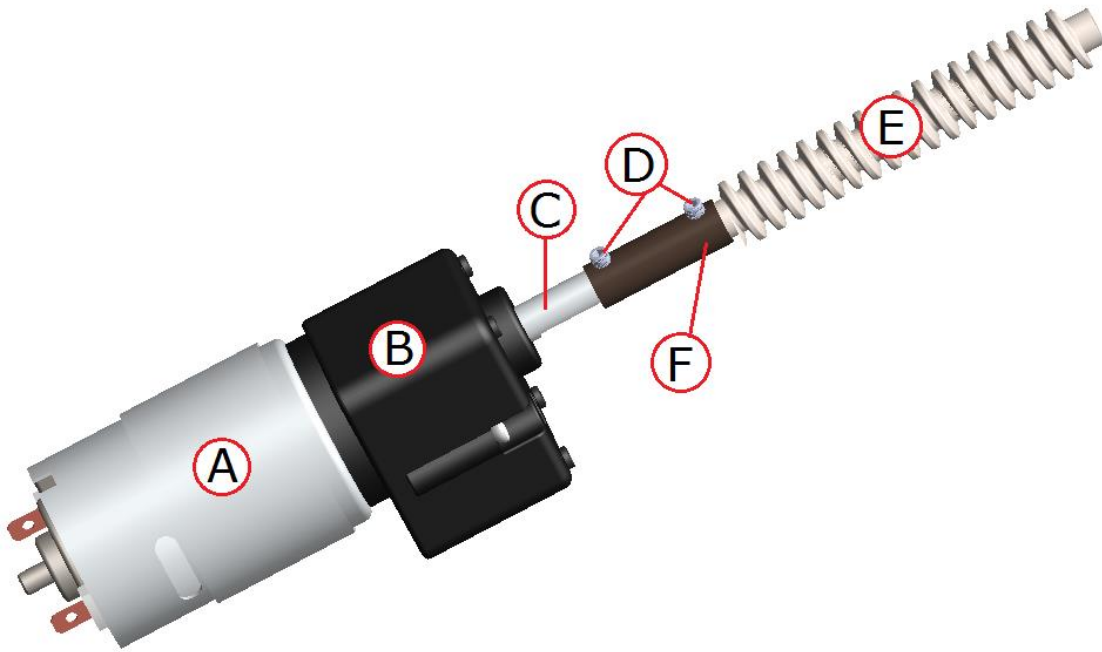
Diseño del acople mecánico que va al motorreductor.
